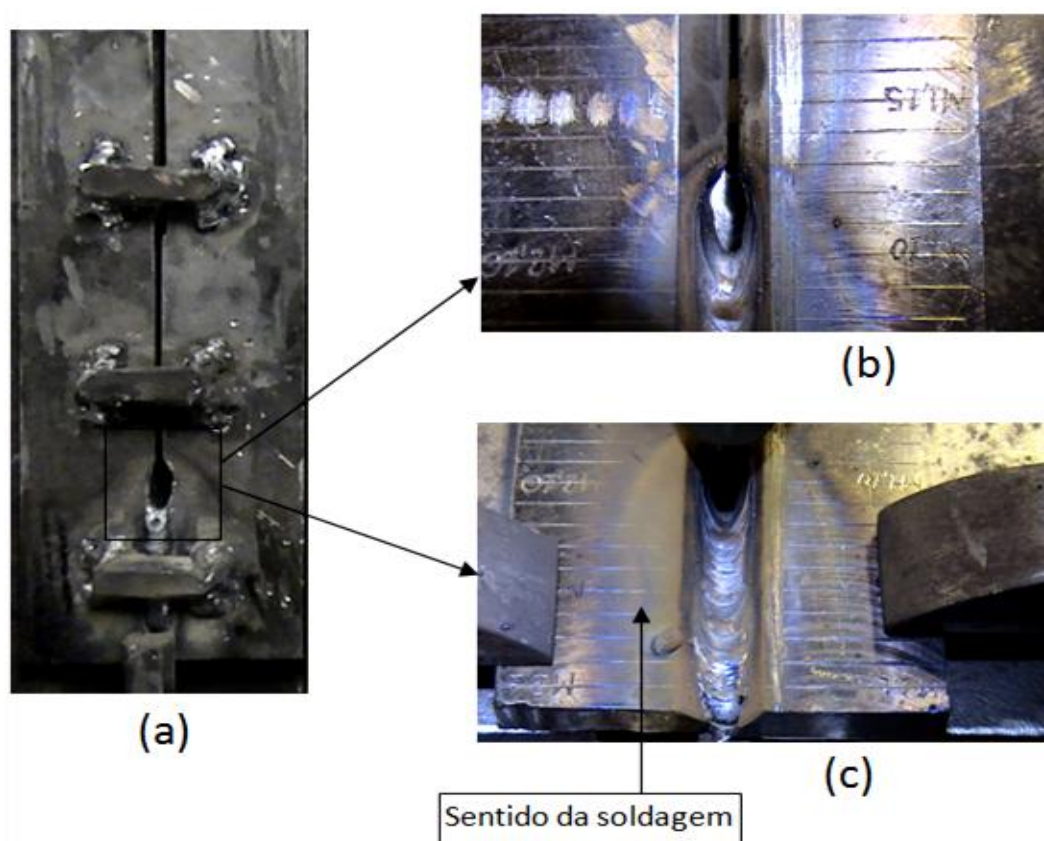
Soldagem na região “sem defeito” e não utilizando a oscilação magnética. (a) vista inferior, (b) e (c) vista superior.
